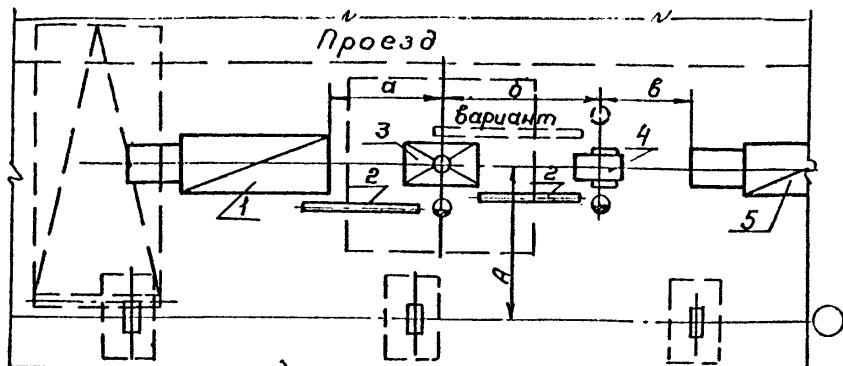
Схема расположения штамповочных линий на базе ПБМ:
